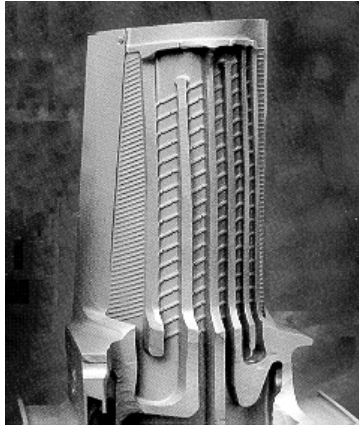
Filmgekühlte Schaufel der ersten Gasturbinen-Laufreihe [1]
